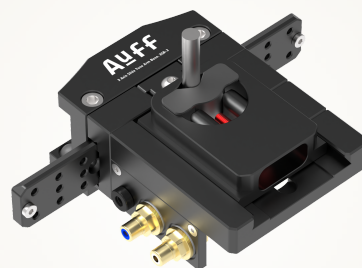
Montaje del adaptador Schick (Ø 8 – Ø 19)
